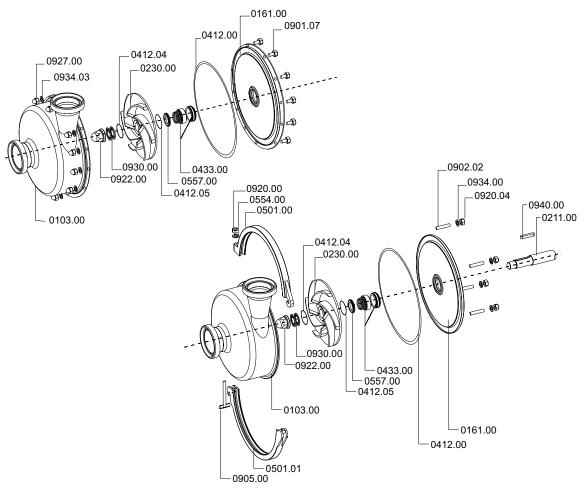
Обзор деталей: насосы с одинарным торцевым уплотнением Вверху: корпус HPM | Внизу: корпус KLM
